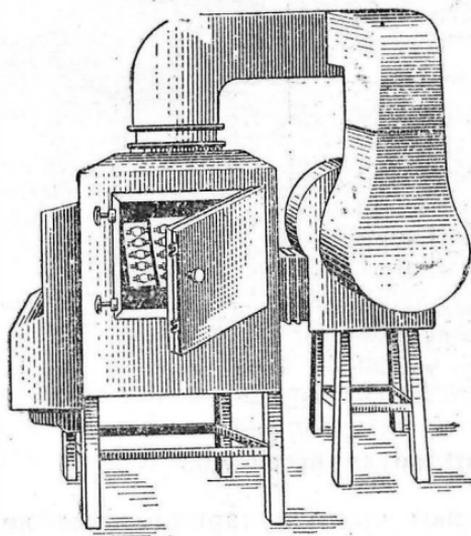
Камера для проверки часов с пылезащищенными корпусами
